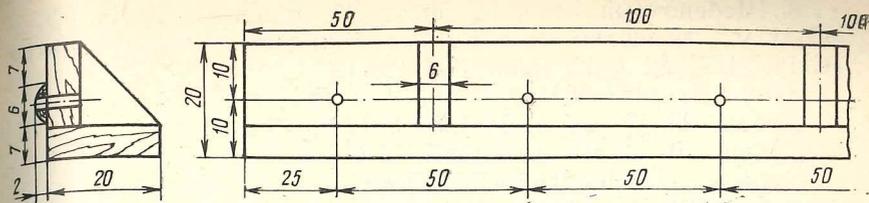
Конструкция шаблона-угольника, используемого для устройства поперечного рабочего шва
